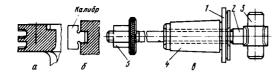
Проверка выработки поршневых канавок и приспособление для ремонта:
